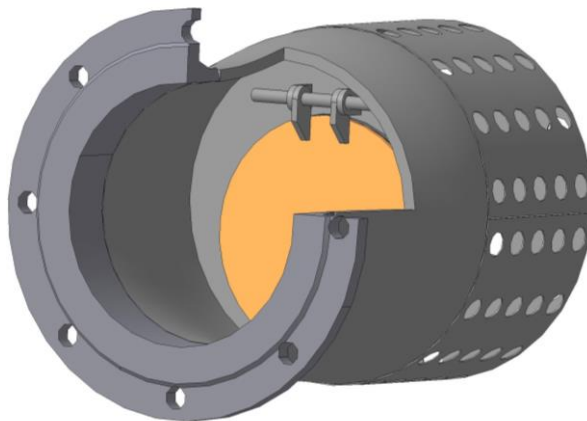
Клапан зворотний приймальний 16ч42р
